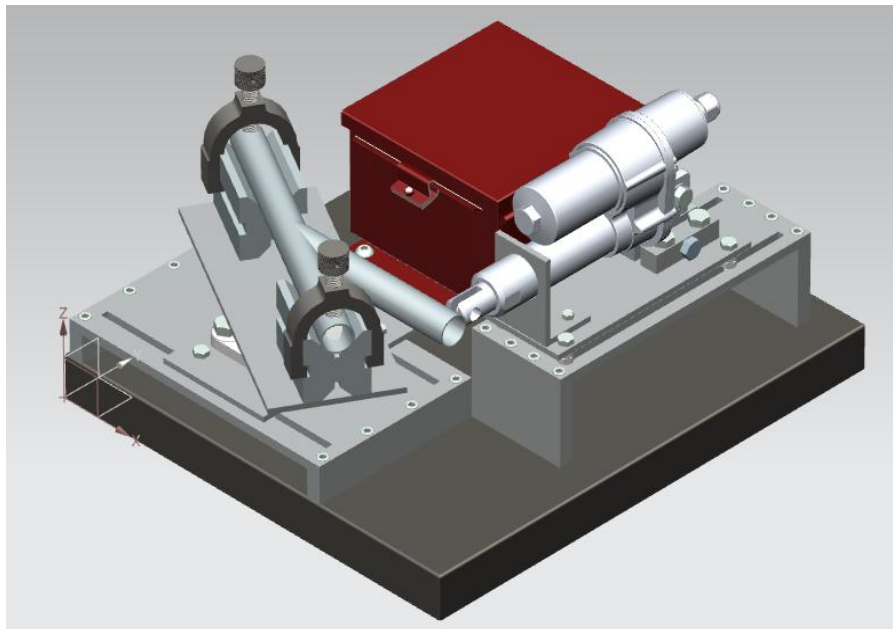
Montaje de la probeta a 30° en la máquina propuesta.
